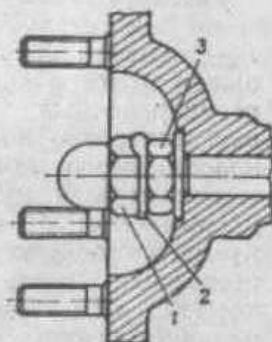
Узел регулировки подшипников ведомого вала колесного редуктора (подшипников колес):
